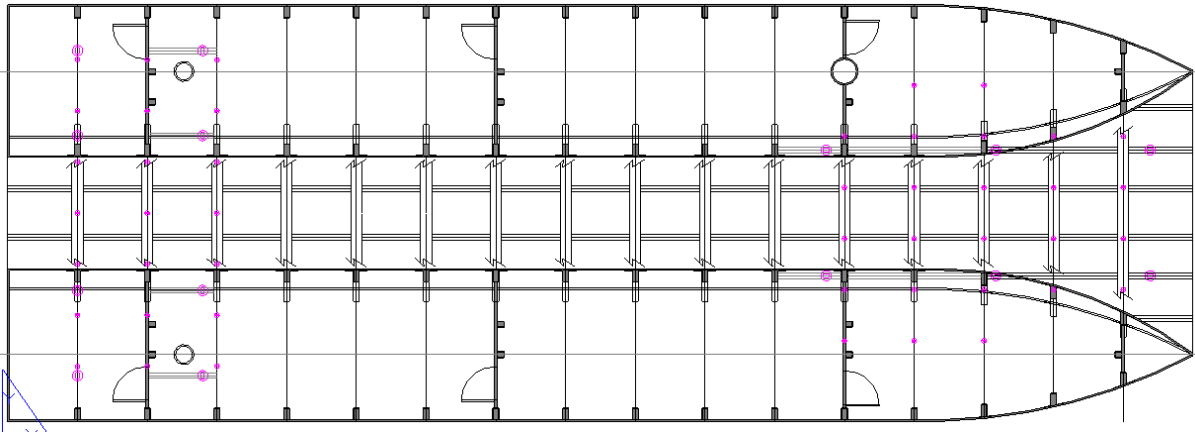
Vista en planta de la ubicación de los anclajes de la carga solapados con los refuerzos de cubierta. Elaboración propia.
